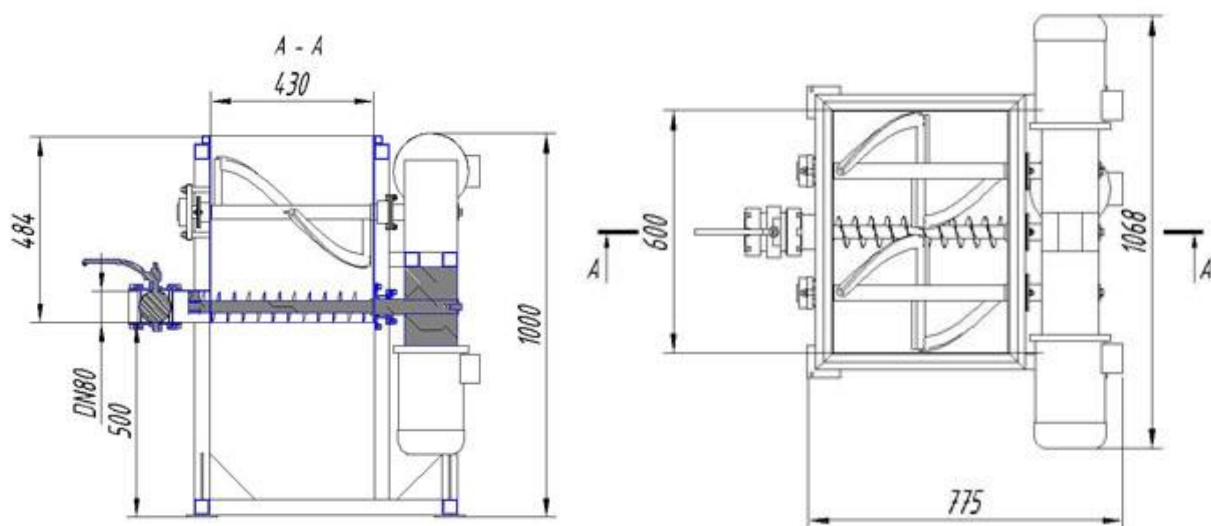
Схема пристрою двоухоторного змішувача з Z образними мішалками
